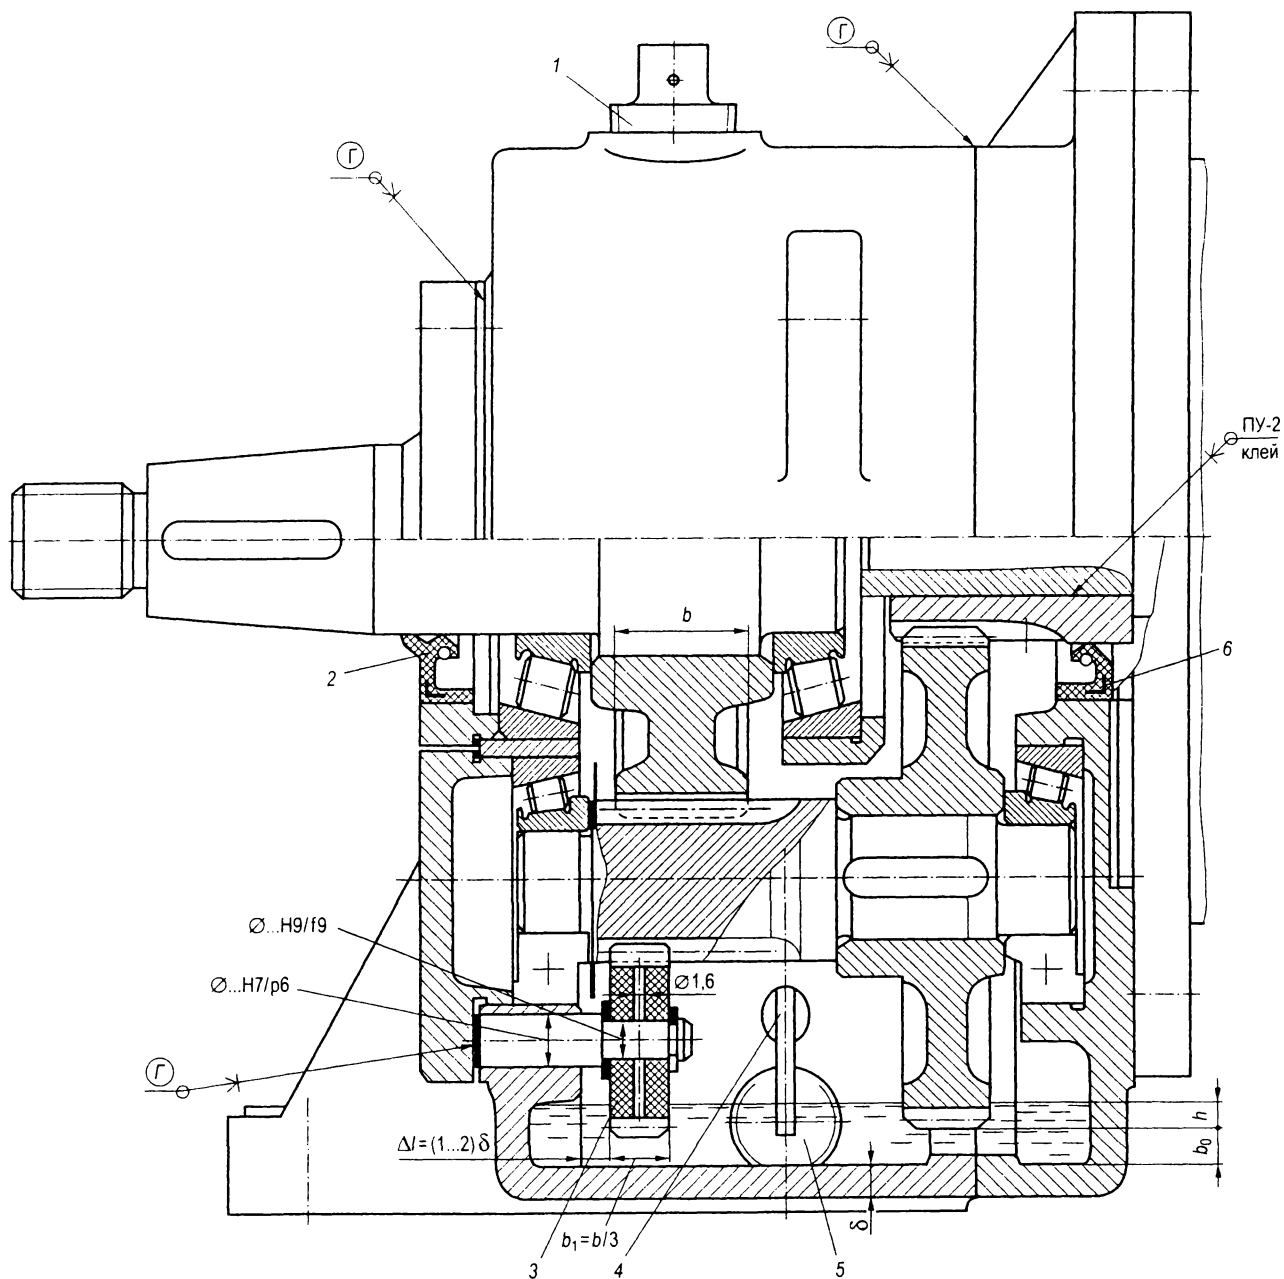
Двухступенчатый соосный мотор-редуктор со смазывающей вспомогательной шестерней [1]:
